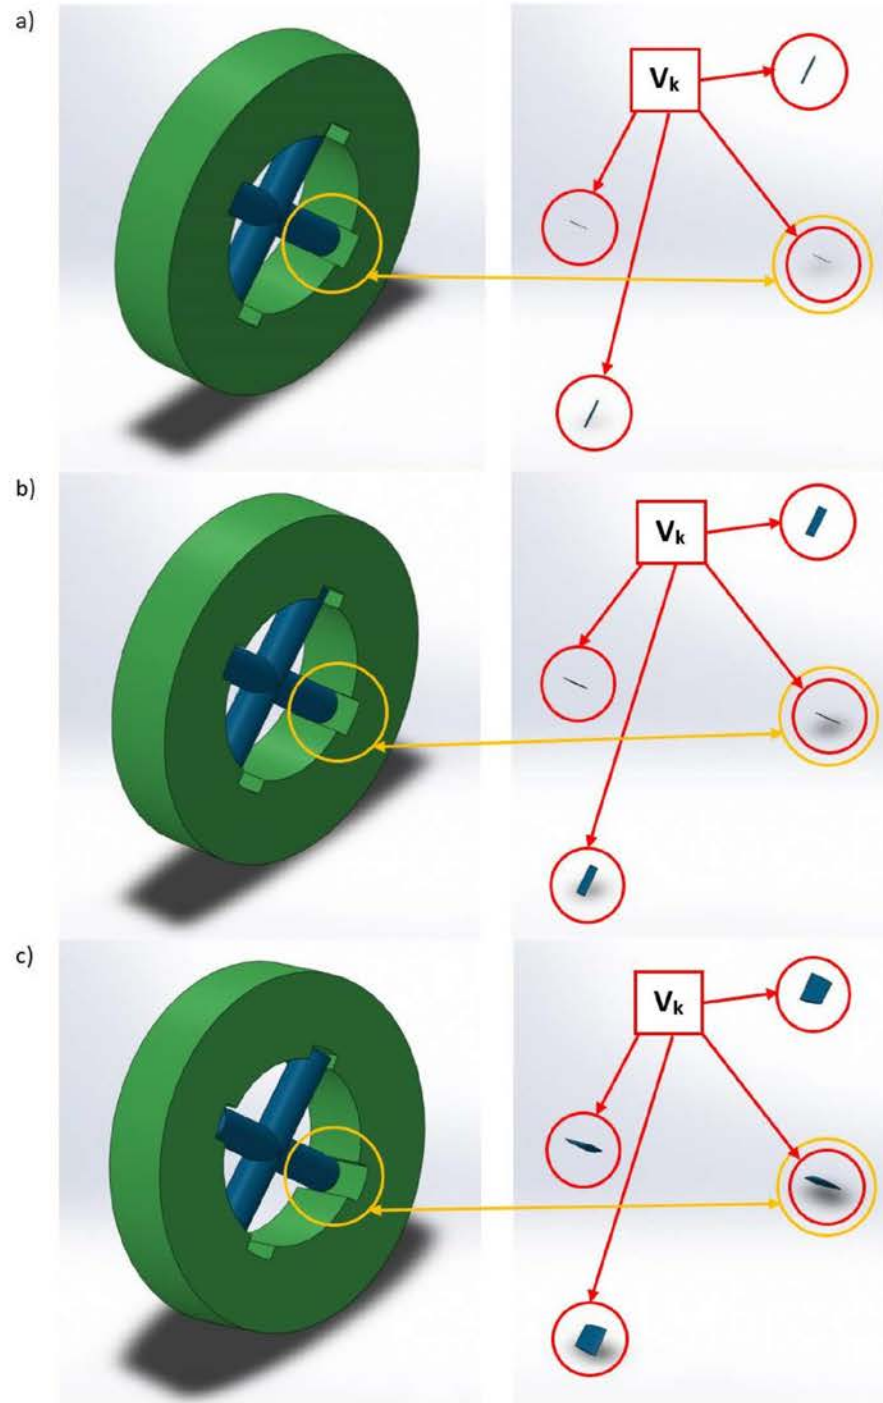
Schemat wahliwego osadzenia koła na wale z wykorzystaniem czterech walców:
